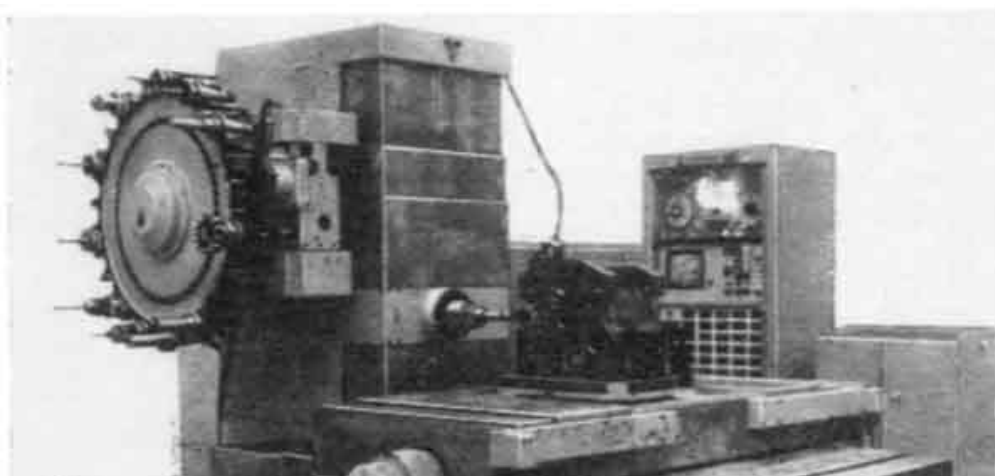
Горизонтальный станок с магазином типа «РУКА» барабанного типа
